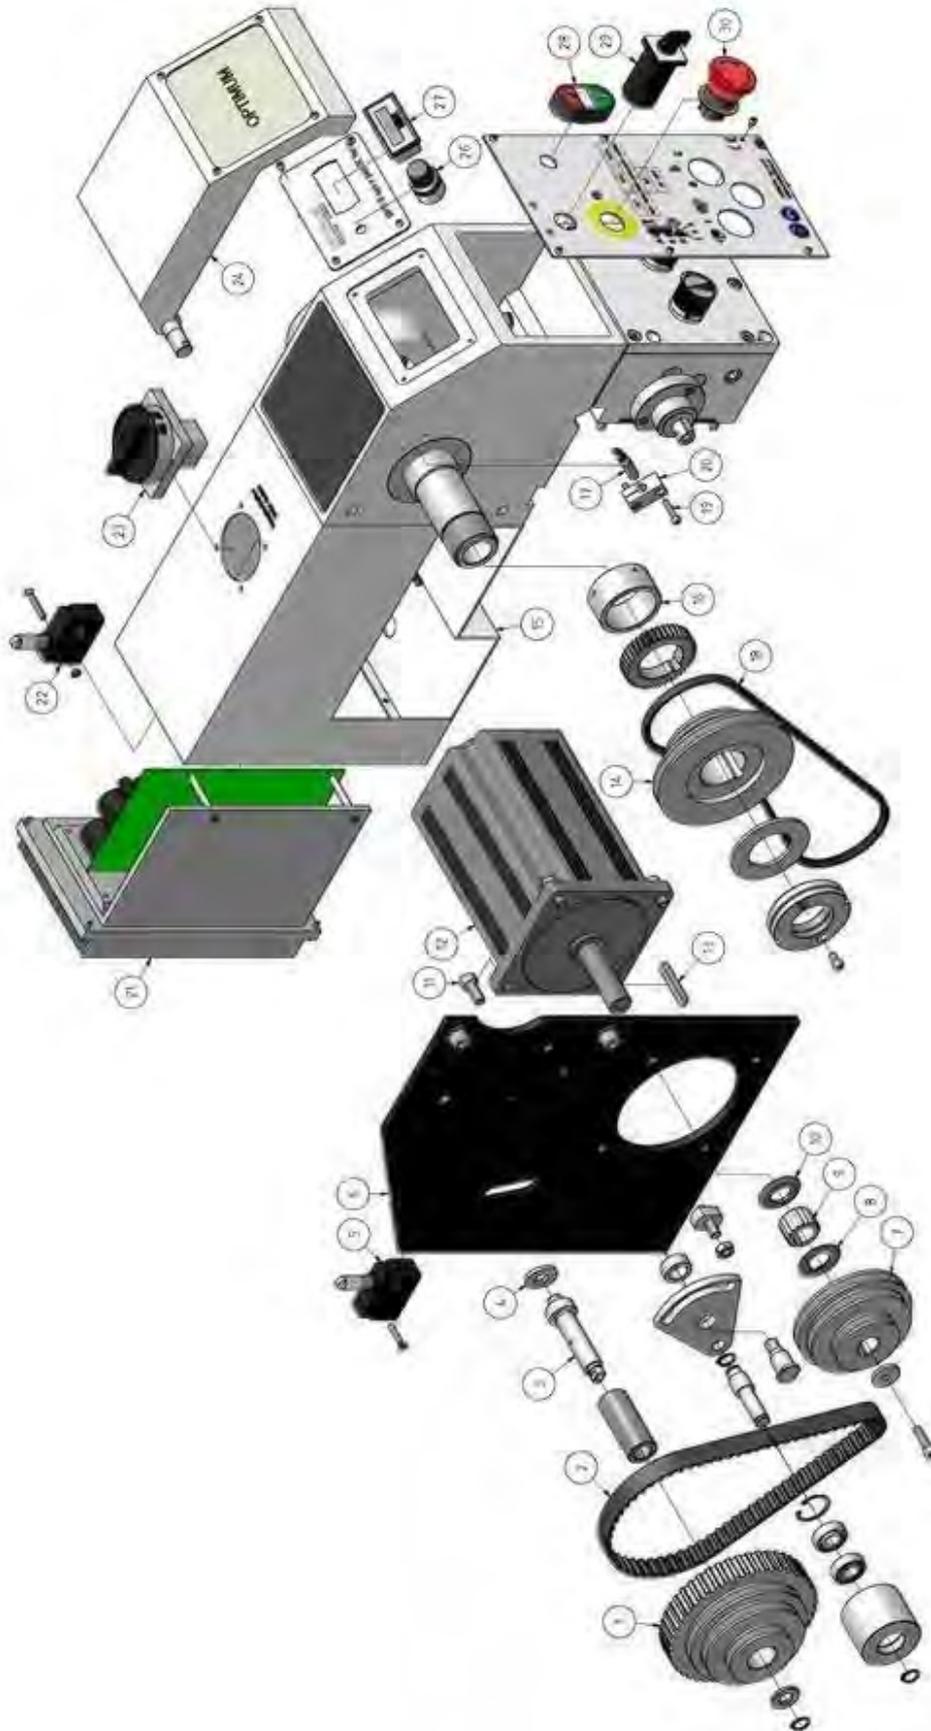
Spindelstock - Cabezal TU 2506 V
